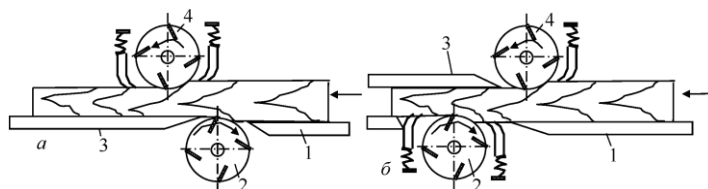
Схеми двостороннього фрезерування: а - фугувально-рейсмусова; б - двурейсмусова
